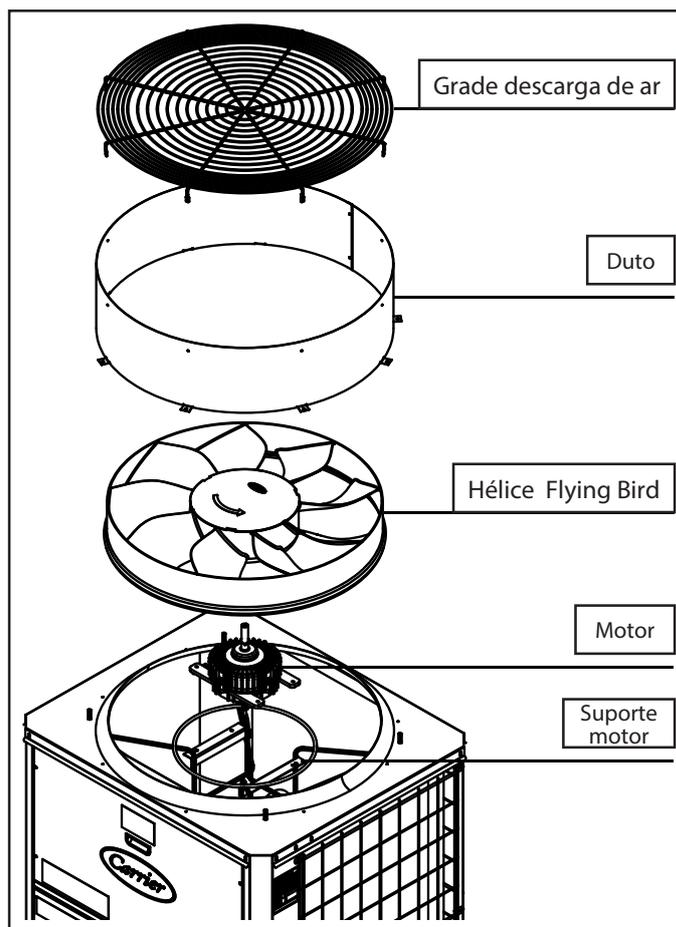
Vista explodida conjunto ventilador das unidades condensadora 38EX/38EV e Hélice Flying Bird
